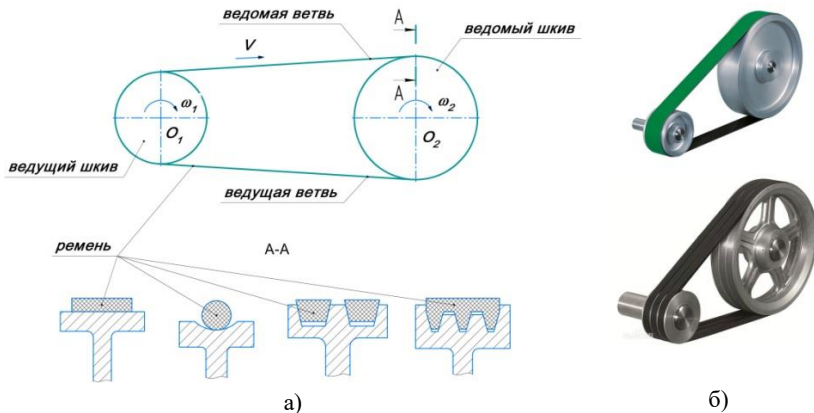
Ременная передача: а) схема; б) внешний вид
